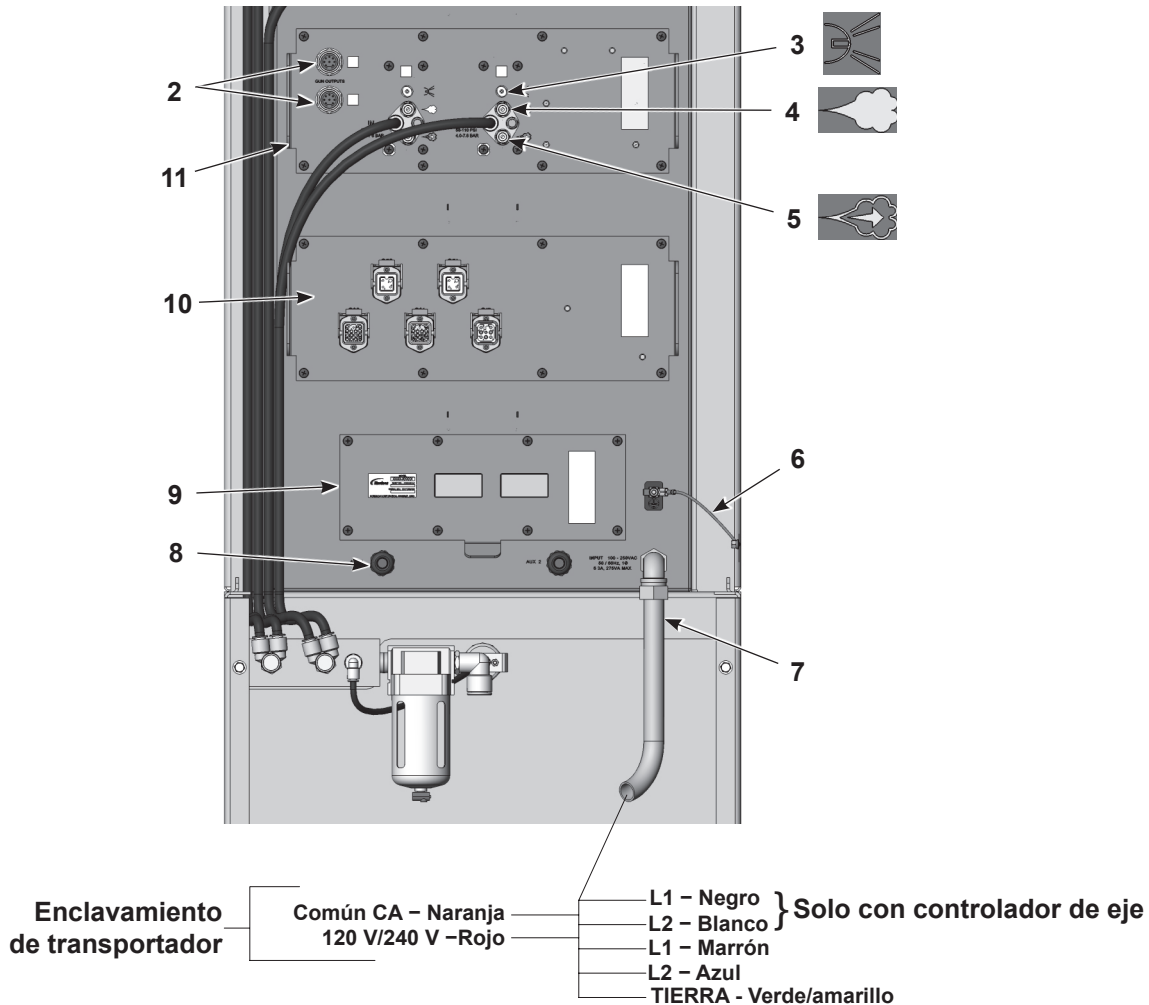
Controlador de pistolas múltiples: conexiones de tensión, aire y pistola (cubierta trasera y rodapié retirados)
